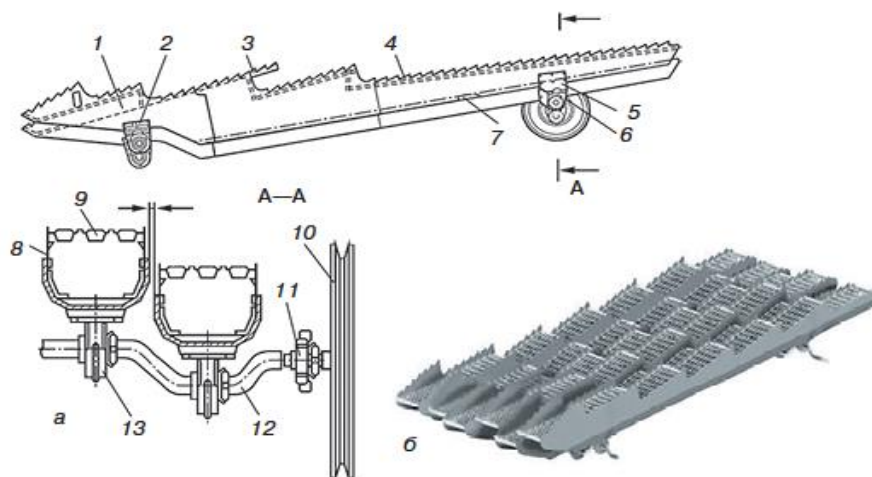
Клавiшний соломотряс (схема встановлення (а) та загальний вигляд (б)): 1 – клавiша; 2 і 5 – кронштейни; 3 і 4 – гребінки; 6 – прокладка; 7 – днище; 8 – корпус клавiші; 9 – жалюзійна поверхня клавiші; 10 – шків приводний; 11 і 13 – підшипники; 12 – колінчастий вал
